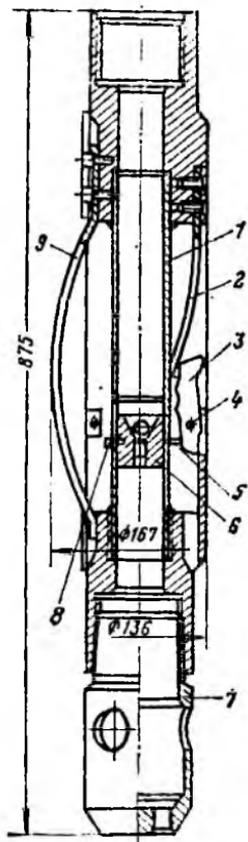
Глубинный механический фиксатор 1ФГМ-168
